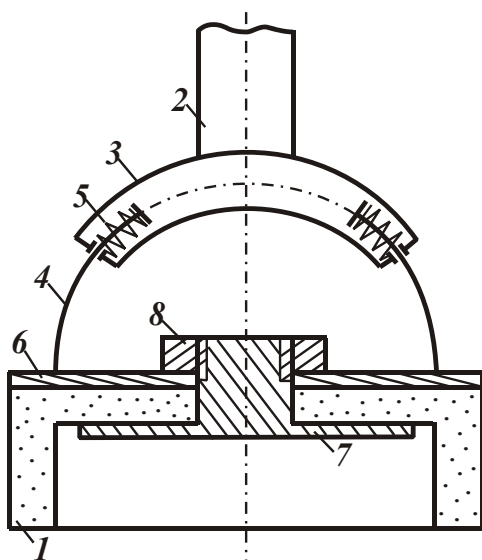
Устройство для обработки поверхностей шлифованием под разными углами: 1 – чашечный шлифовальный круг; 2 – вал, передающий вращение; 3 – сферический цилиндр; 4 – сферические штоки; 5 – пружина; 6 – корпусный диск с закрепленными сферическими штоками; 7 – крепежная шайба с посадочным валом и резьбой; 8 – гайка для крепления.
